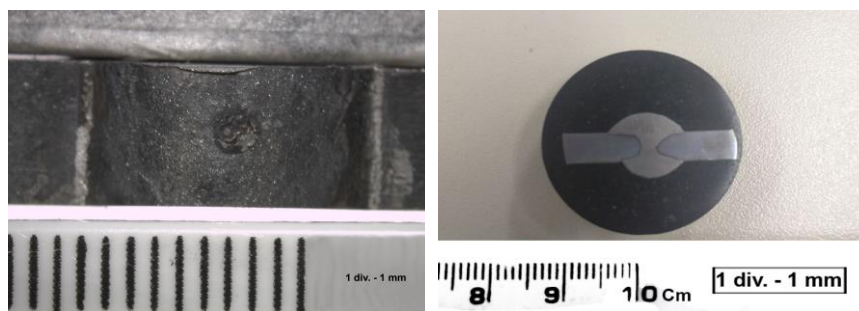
Detalhe superfície e perfil do cordão de solda do CP 2.
